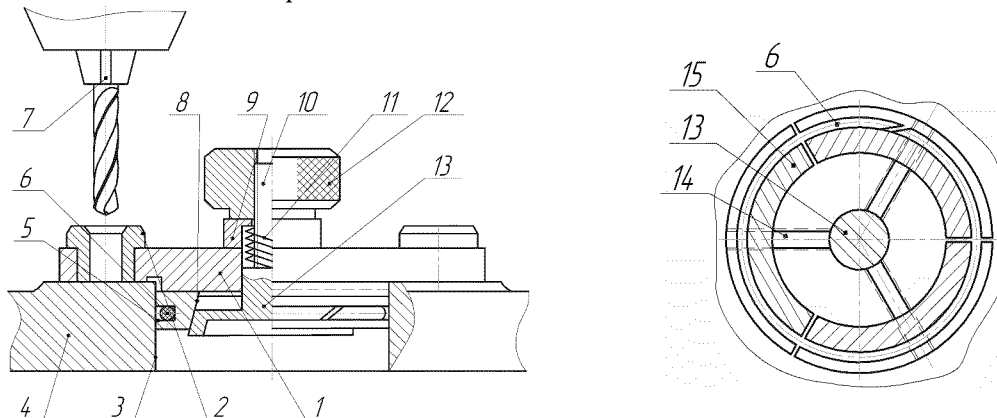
Накладний переналагоджувальний сверлильний кондуктор
